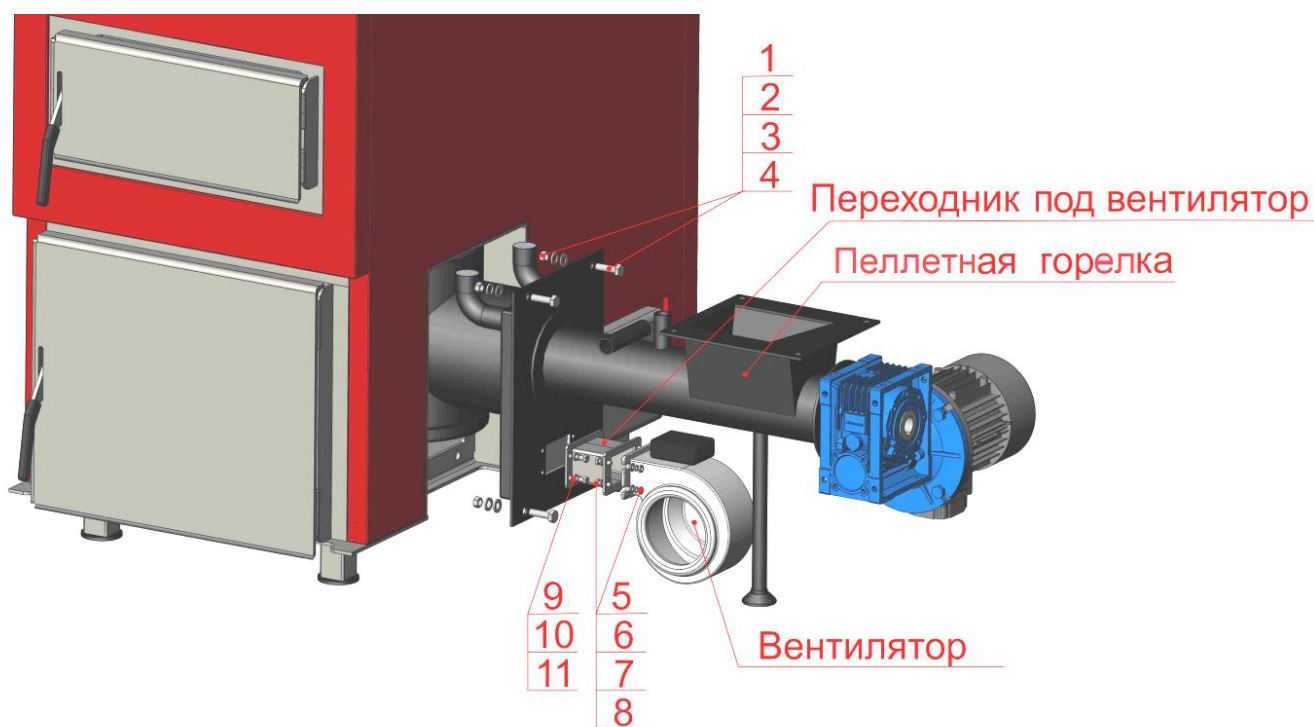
Схема монтажа пеллетной горелки и вентилятора.
